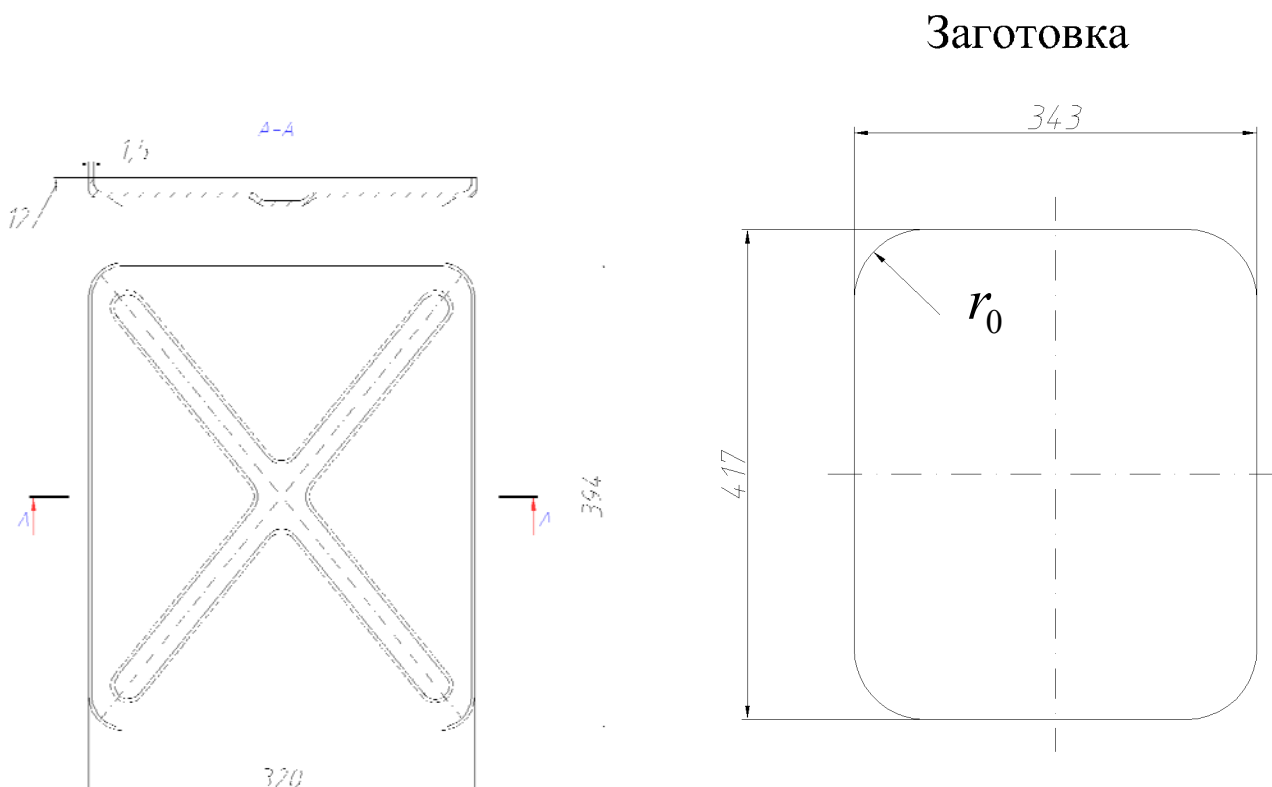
Коробчатая деталь «Крышка» и заготовка со скругленными углами
